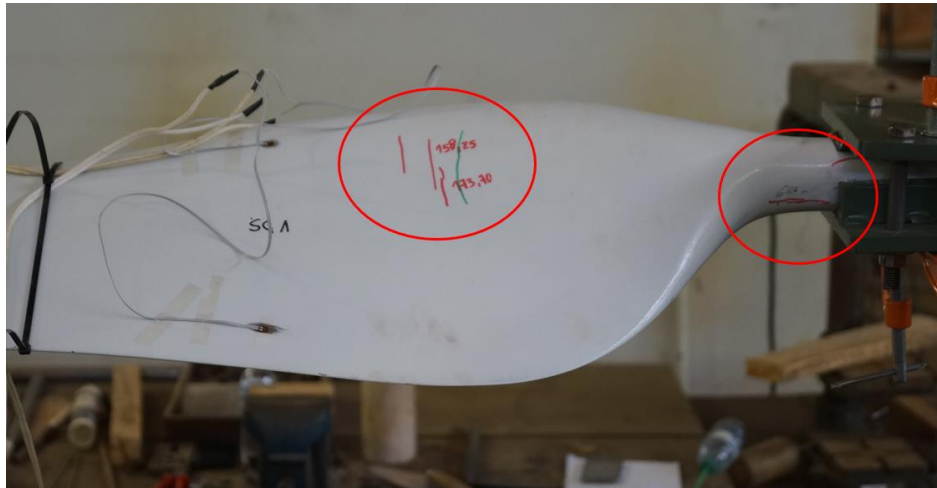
Surgimento das primeiras fissuras superficiais no Ensaio 3.
